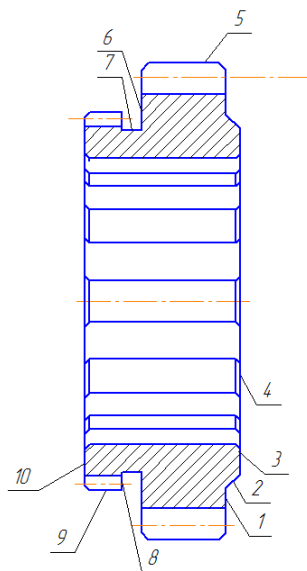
Поверхні шестерні 78-60567Б
